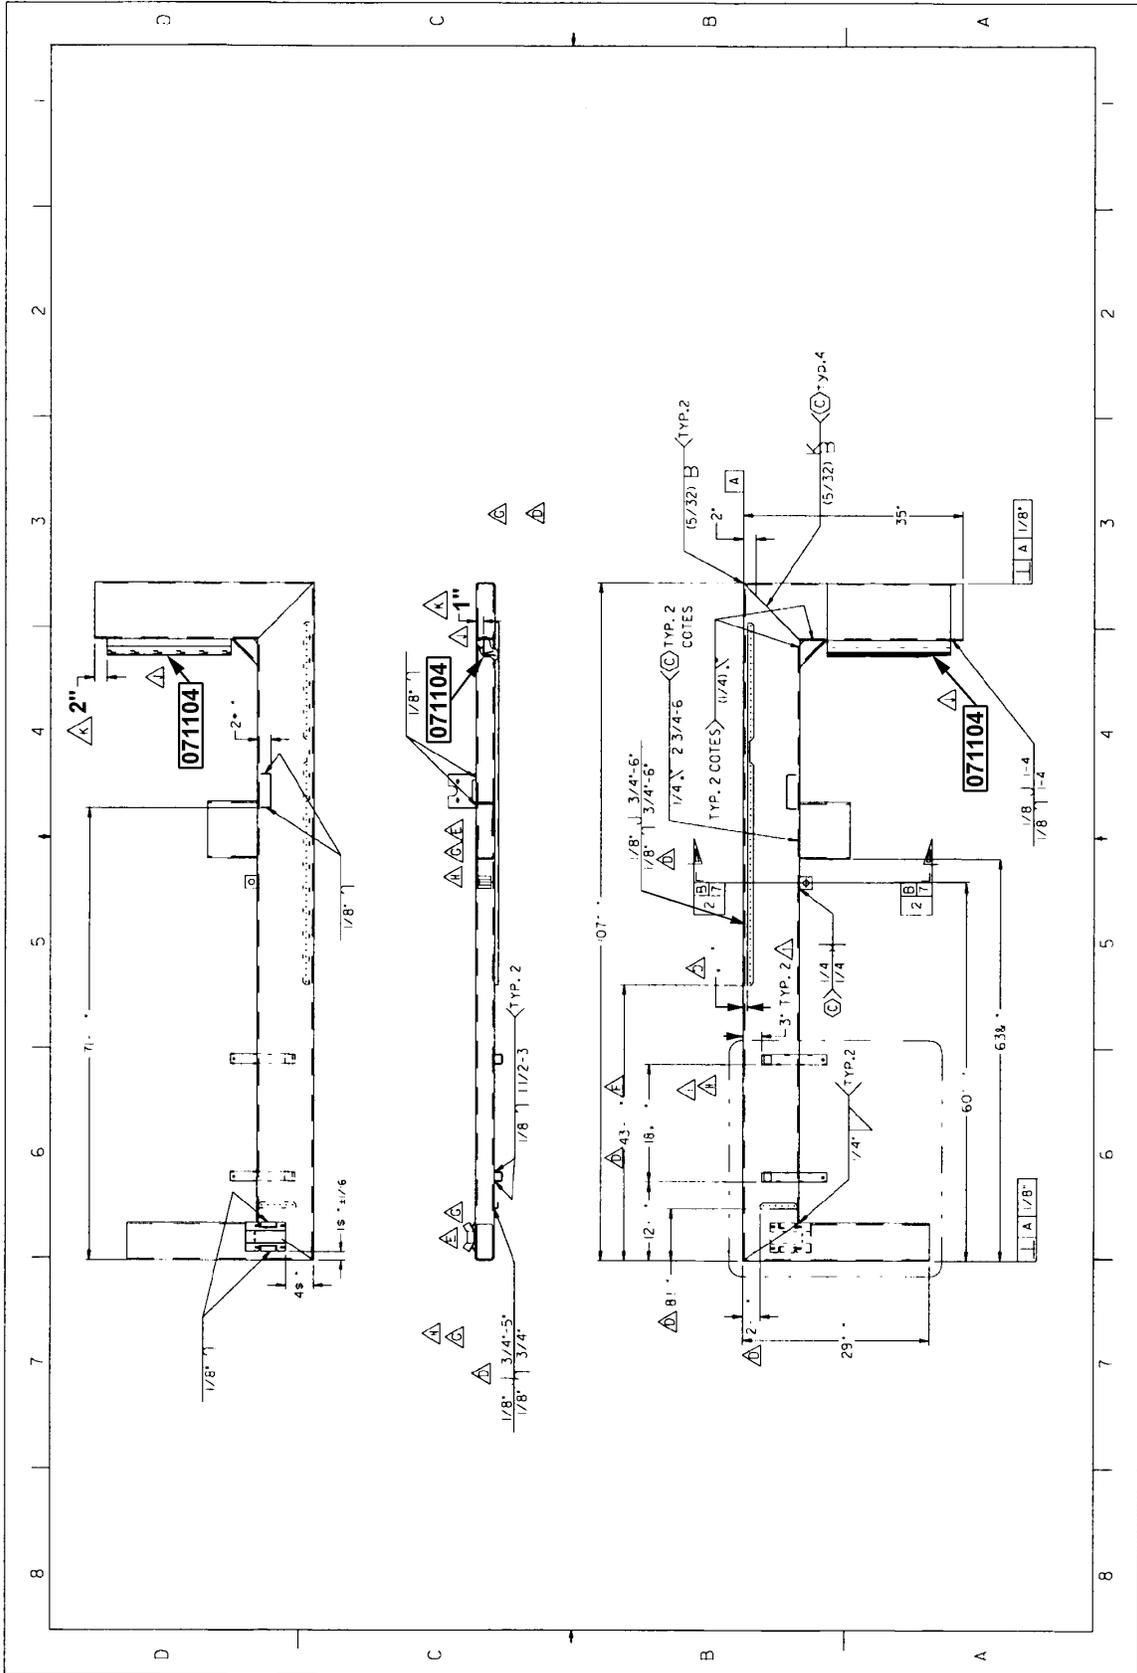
INSTALLATION DU SUPPORT LATÉRAL DROIT SUR LE LONGERON
